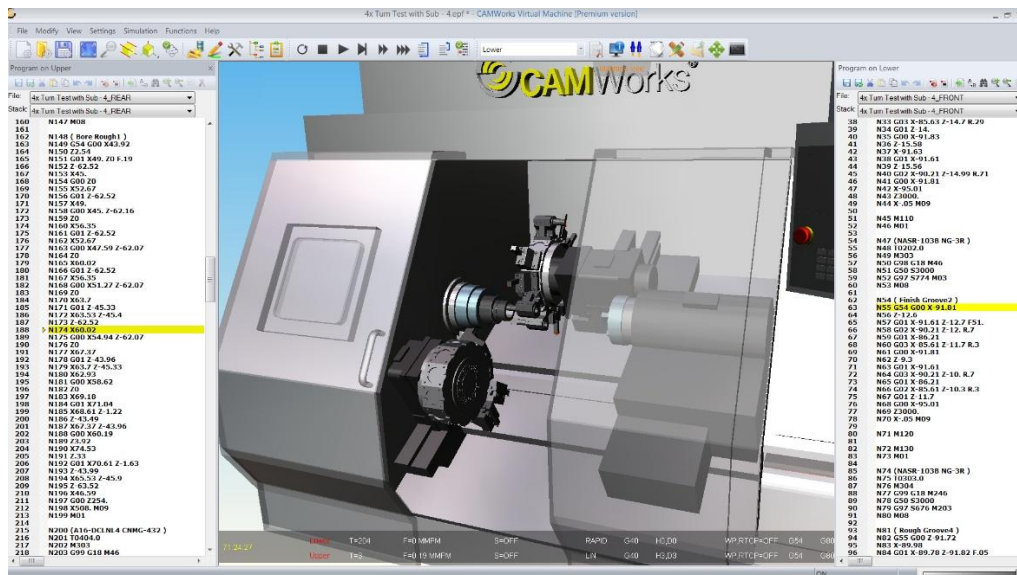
Імітаційна модель обробки деталі «Корпус центрової бабки» на оброблювальному центрі MAST\_MM648\_S16
